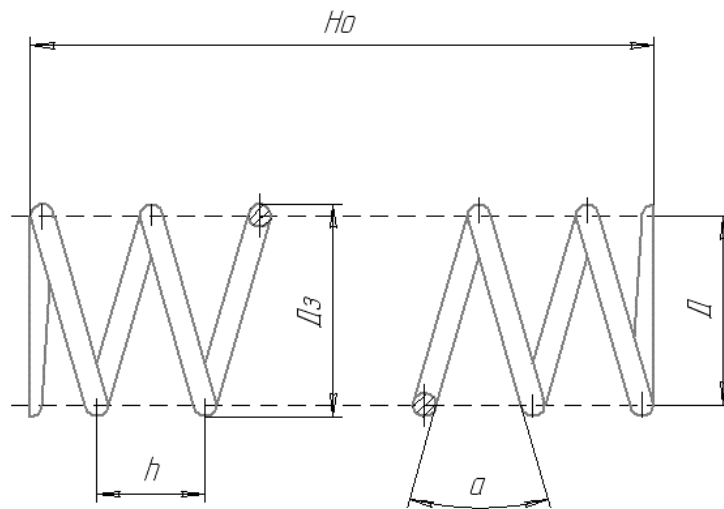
Схема пружини стискання із циліндричним перерізом
